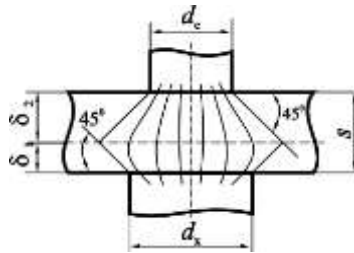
Схема поля струму для розрахунку опору деталі з неоднаковими розмірами контактів
